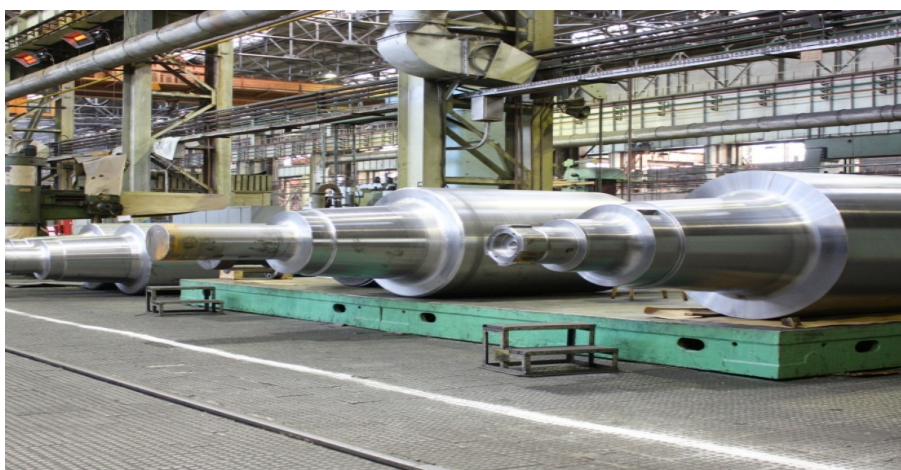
Валки стальные кованные для холодной и горячей прокатки металлов
